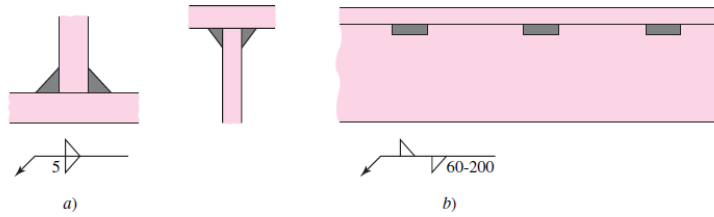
Detalle de soldadura de filete. Fuente: Budynas, Richard G.; Nisbett, J. Keith, pág.459 [31].
